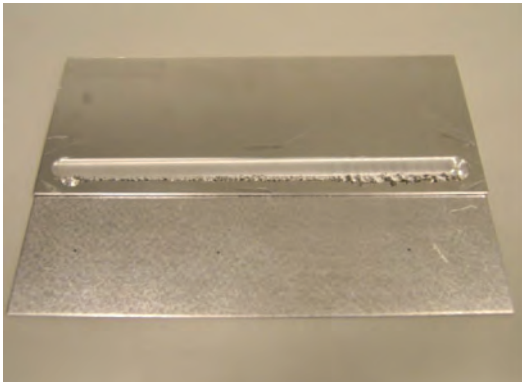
Chapas de aluminio y acero soldadas por FSW
